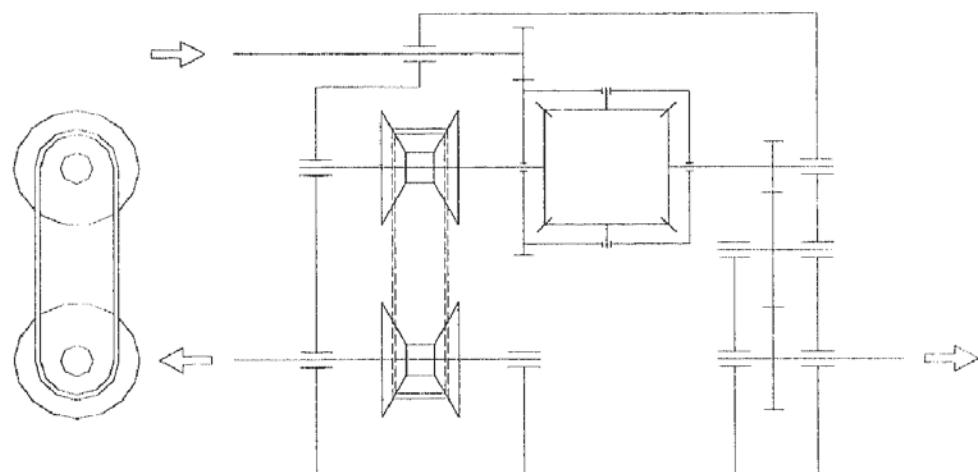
Схема одноступенчатой раздаточной коробки с межосевым дифференциалом для машины с колесной формулой 6×6
